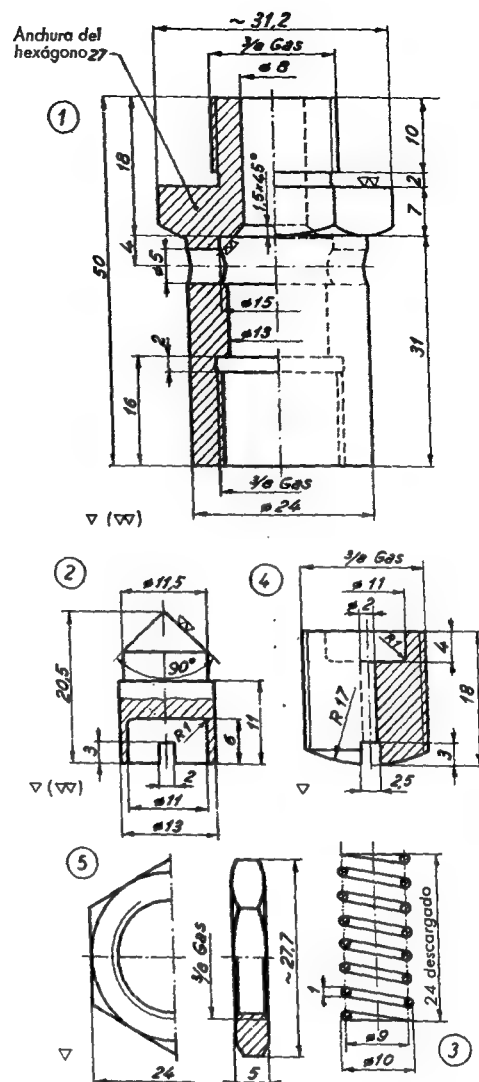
Válvula de resorte helicoidal, dibujo de conjunto y detalles.
